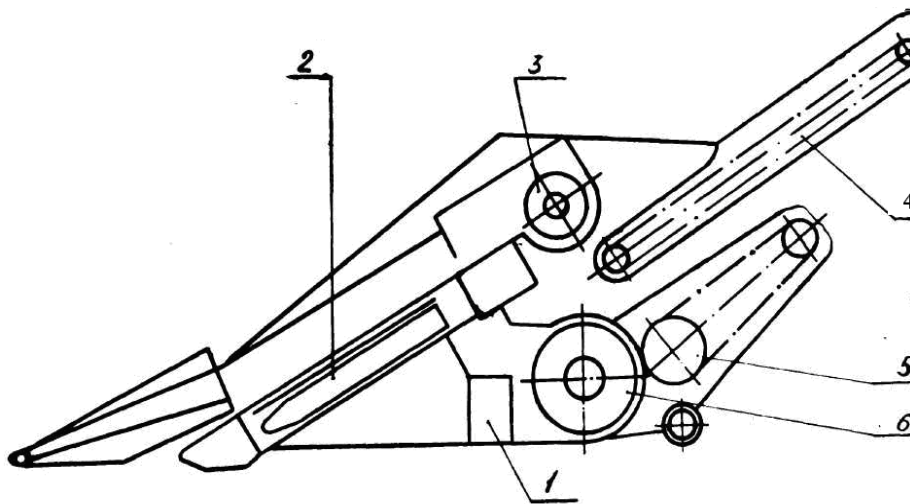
Схема жатки 2-го виду: 1 – різальний апарат з подрібнювальним механізмом; 2 – качано-відокремлювальний механізм; 3 - качано напрямний шнек; 4,5 - елеватори; 6 - стебловий шнек
